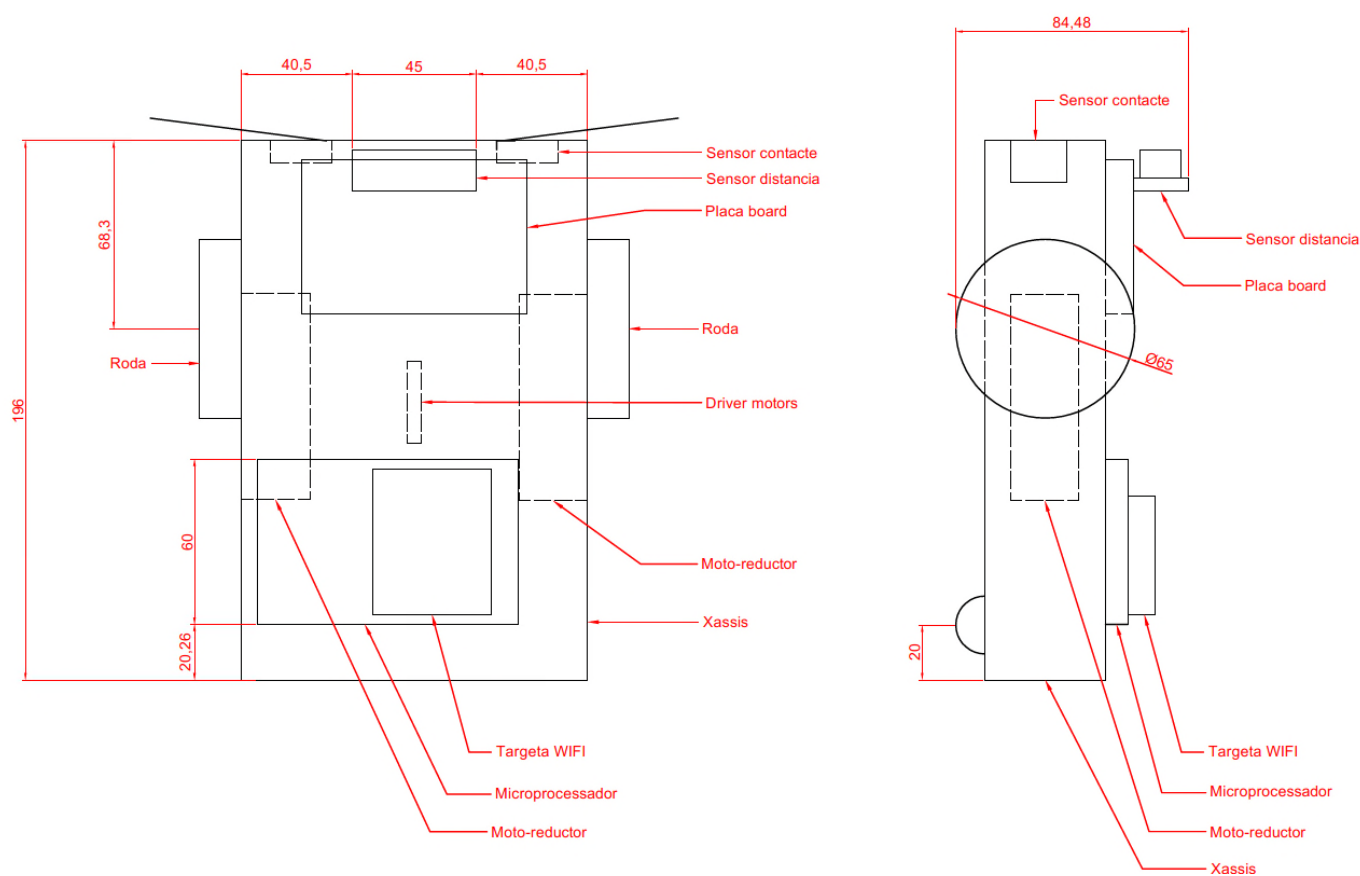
Dimensions generals del vehicle: esquerra vista en planta, dreta vista en alçat (unitats en mm)
